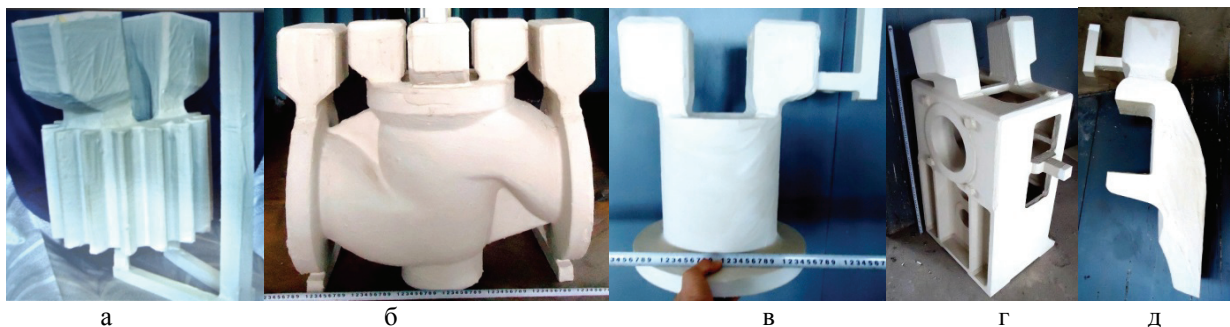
Моделі сталевих виливків: а — шестерні; б — засувки; в — патрубкa; г, д — корпусних виливків
